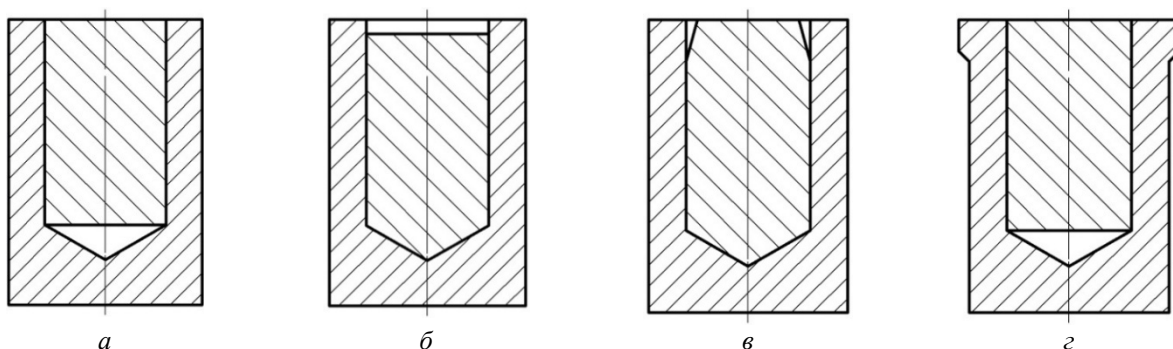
Складні зразки різної форми (а-г) для видавлювання заготовки біметалічного плунжера
